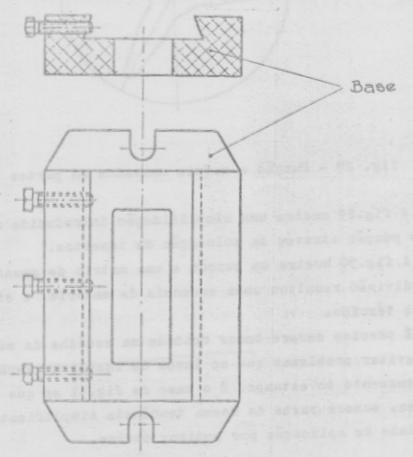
Fixação de uma placa de corte com encaixe do tipo prismático
